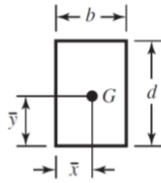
Soldadura a filete de perfil rectangular.
